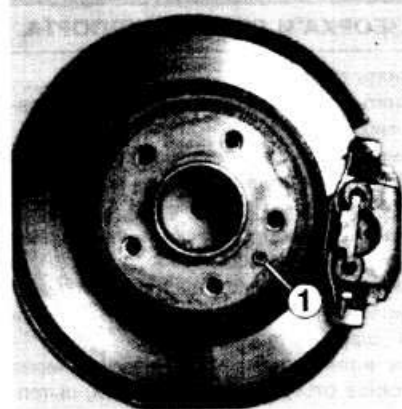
Болт 1 крепления тормозного диска заднего колеса
